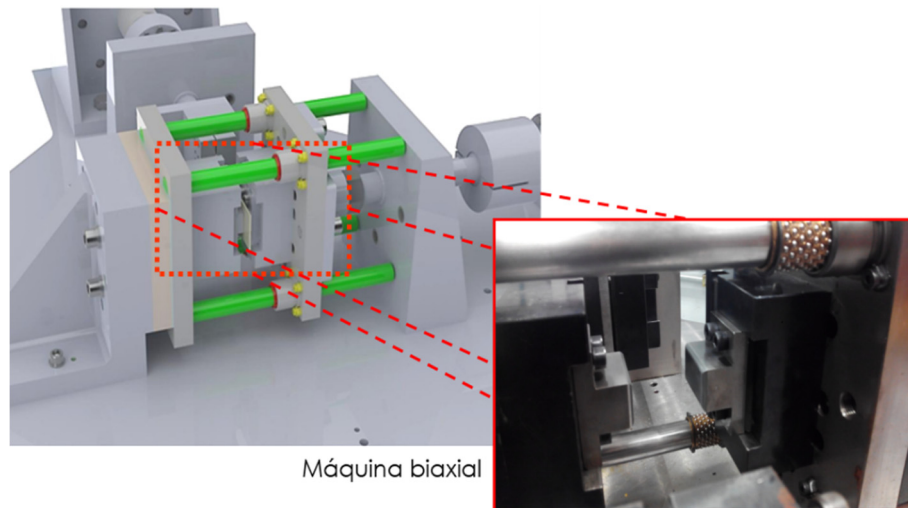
Colocación del utillaje de ensayo de Strip Drawing test sobre la máquina biaxial.
